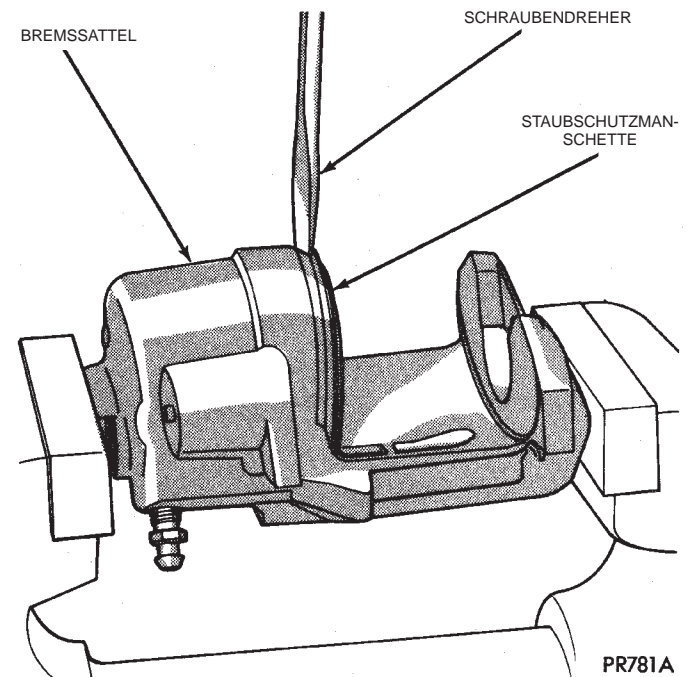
Ausbau der Staubschutzmanschette des Bremssattelkolbens
